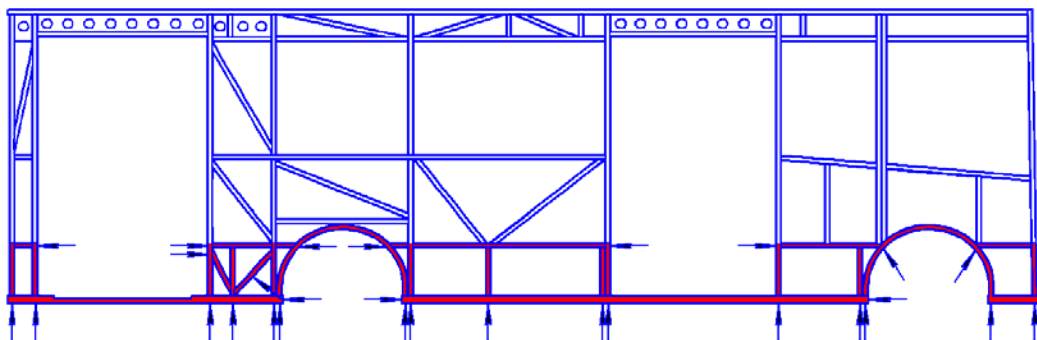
Схема обробки скритих порожнин каркасу правої боковини
